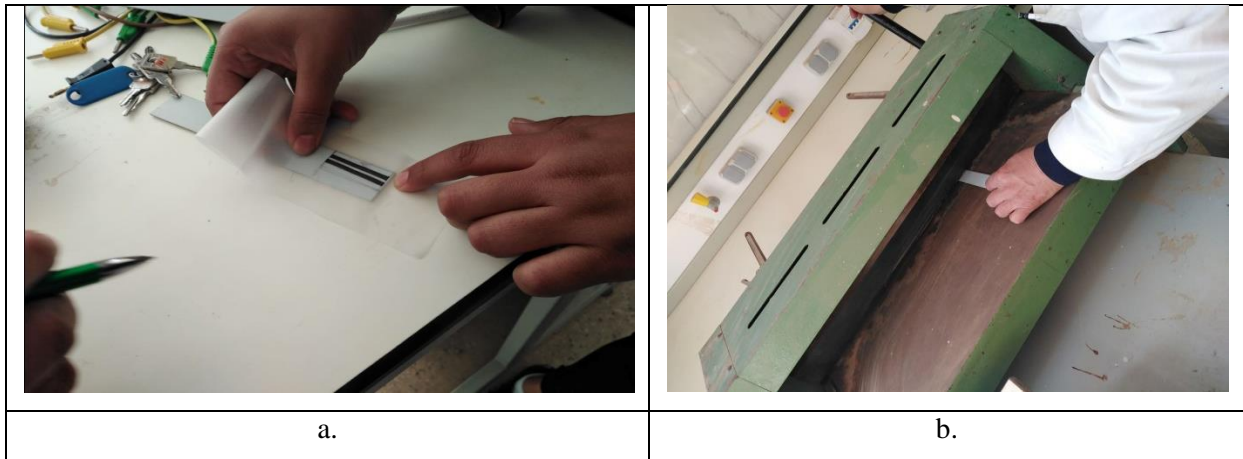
(a) Dessin de la carte PCB sur un papier transparent. (b) coupe la carte PCB par la machine guillotine.
